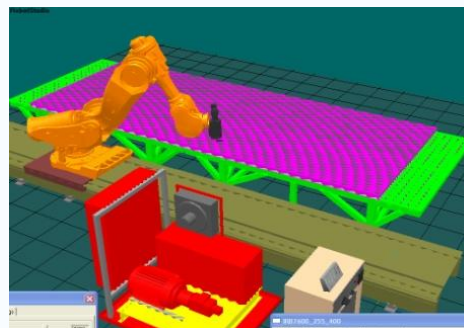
Estación robótica de trabajo para Soldadura FSW
